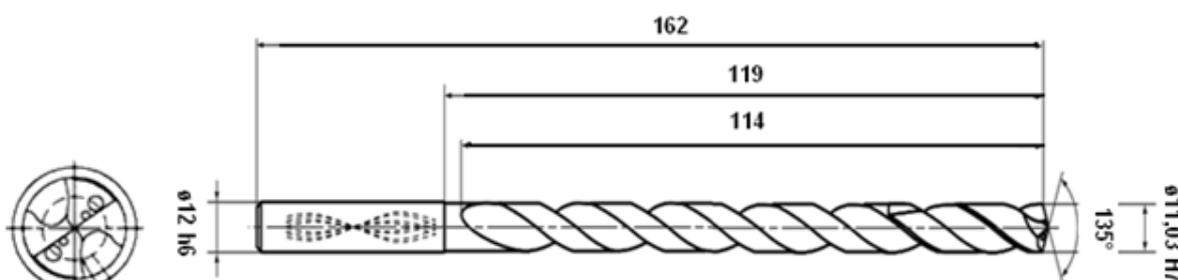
Hartmetallbohrer mit 4 Kühlbohrungen
